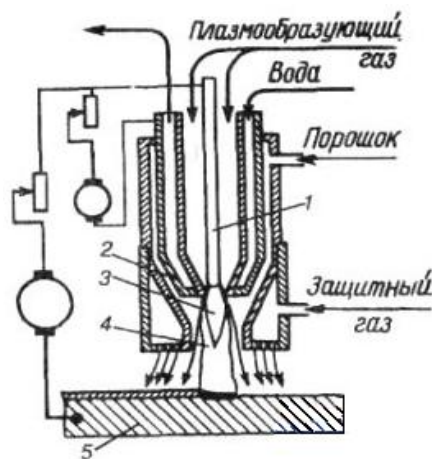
Схема плазменной наплавки с вдуванием порошка в дугу:
